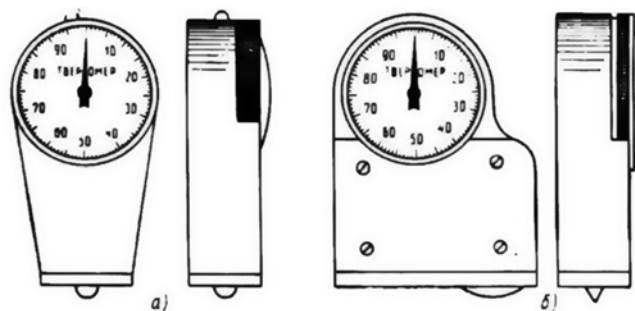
Твердомеры для определения поверхностной твердости литейных форм.
